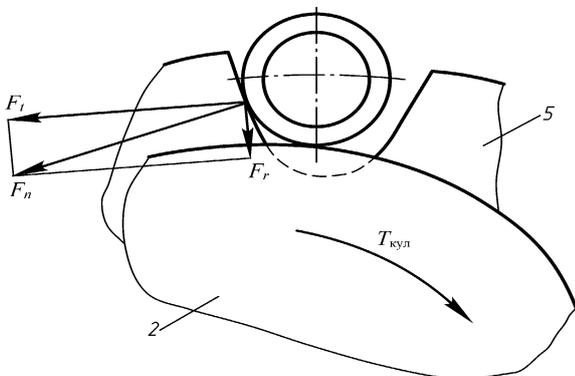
Схема взаимодействия звеньев волновой зубчатой передачи с невращающейся втулочно-роликковой цепью: 2 – кулачок (генератор волн); 5 – ведомое зубчатое колесо
